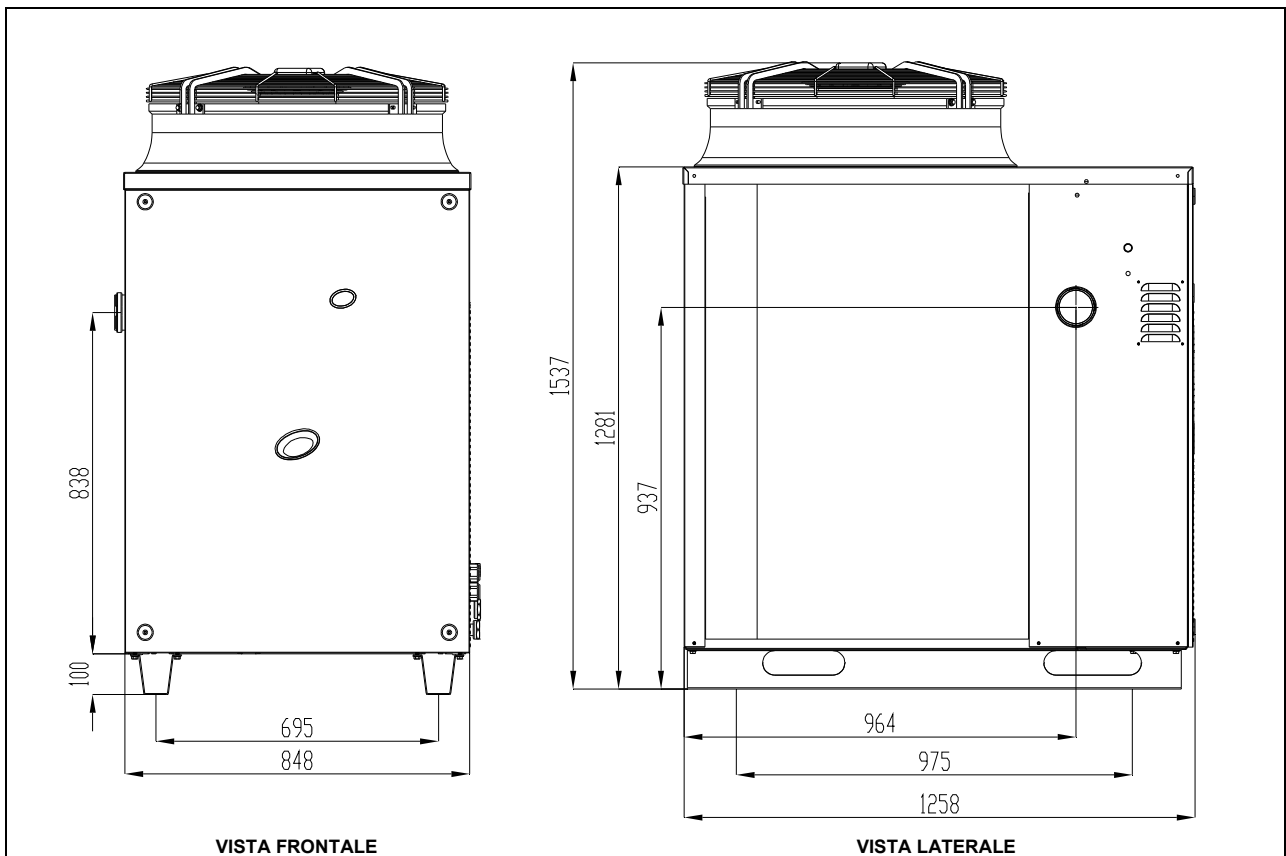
Dimensioni unità GAHP-A "S" - vista frontale e laterale (quote espresse in mm)
